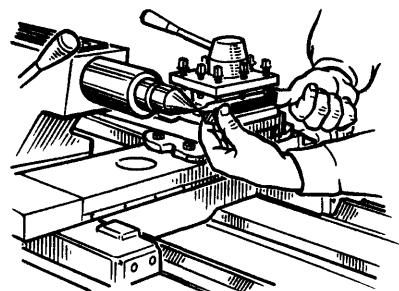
Установка резца в резцедержателе по оси центров станка
